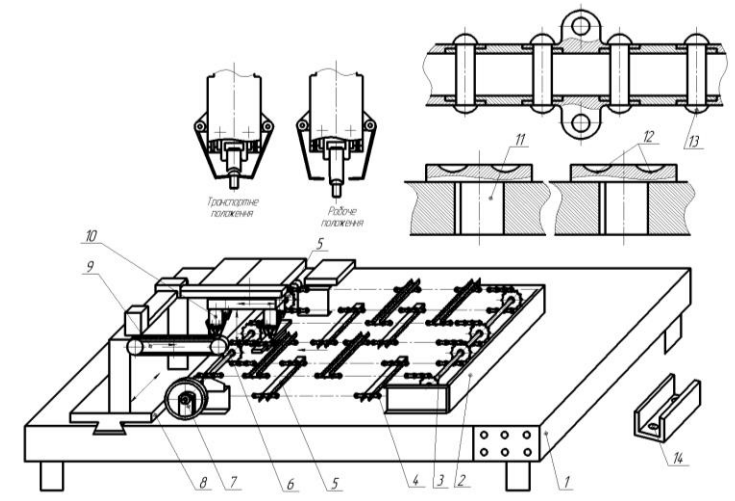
Стенд для складання ланцюгово-планчастих полотен транспортерів [276]: 1 – плита; 2 – підставка; 3 – ведений вал; 4 – ланцюг; 5 – П-подібні планки; 6 – ведучий вал; 7 – привідний механізм; 8 – направляюча стола; 9 – механізм подачі заклепок; 10 – шпindelі клепацьких головок; 11 – заклепки
